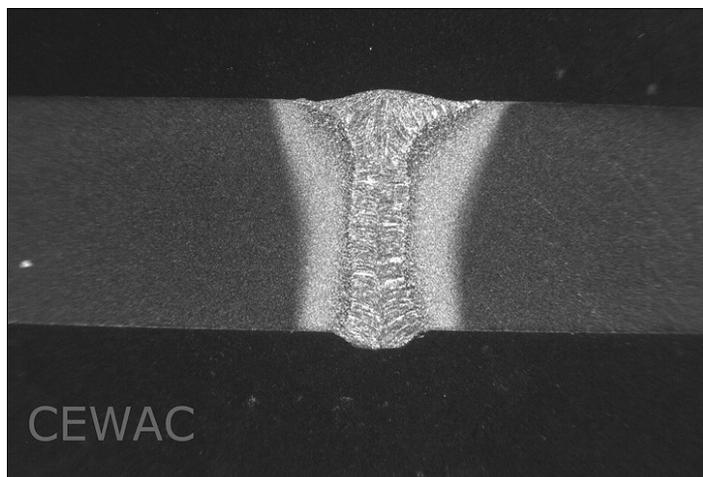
soudure HLW bout-à-bout d'acier (6 mm) à 0,6 m/min
